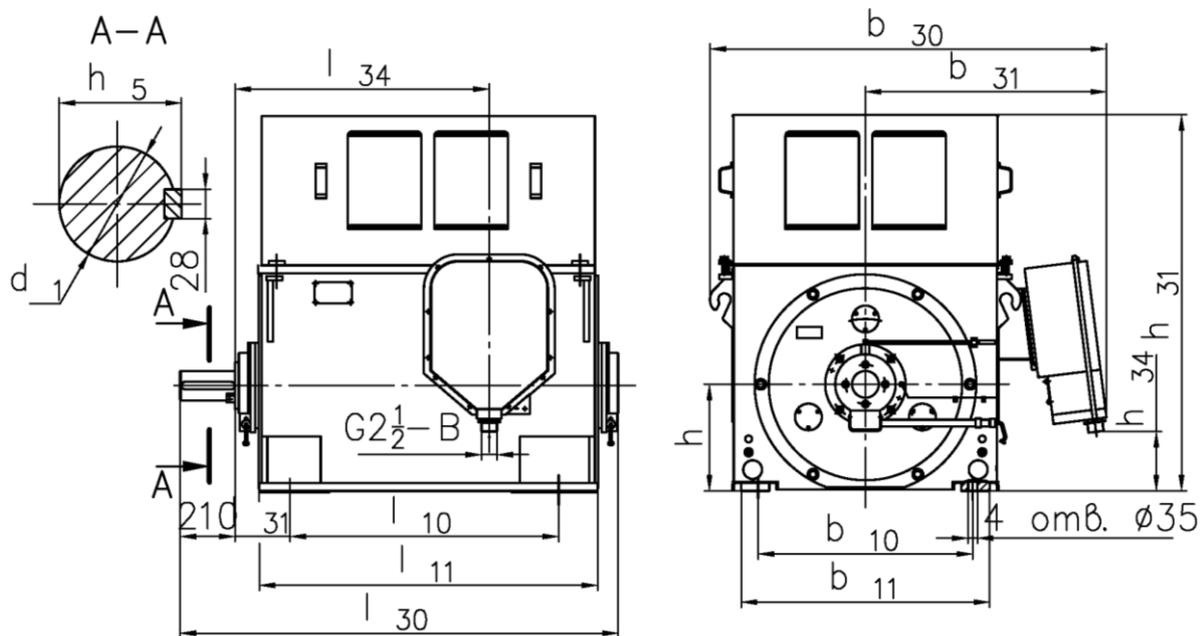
Электродвигатели серии А со сварной коробкой
